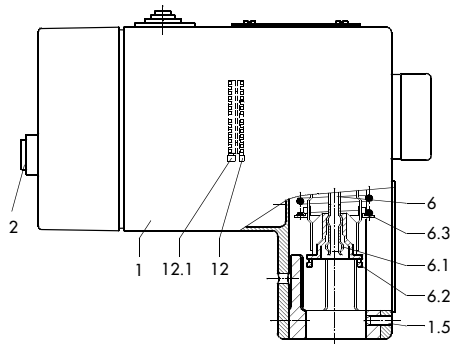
· Typ 5822-10, -20, -30, -40 Wirk-
